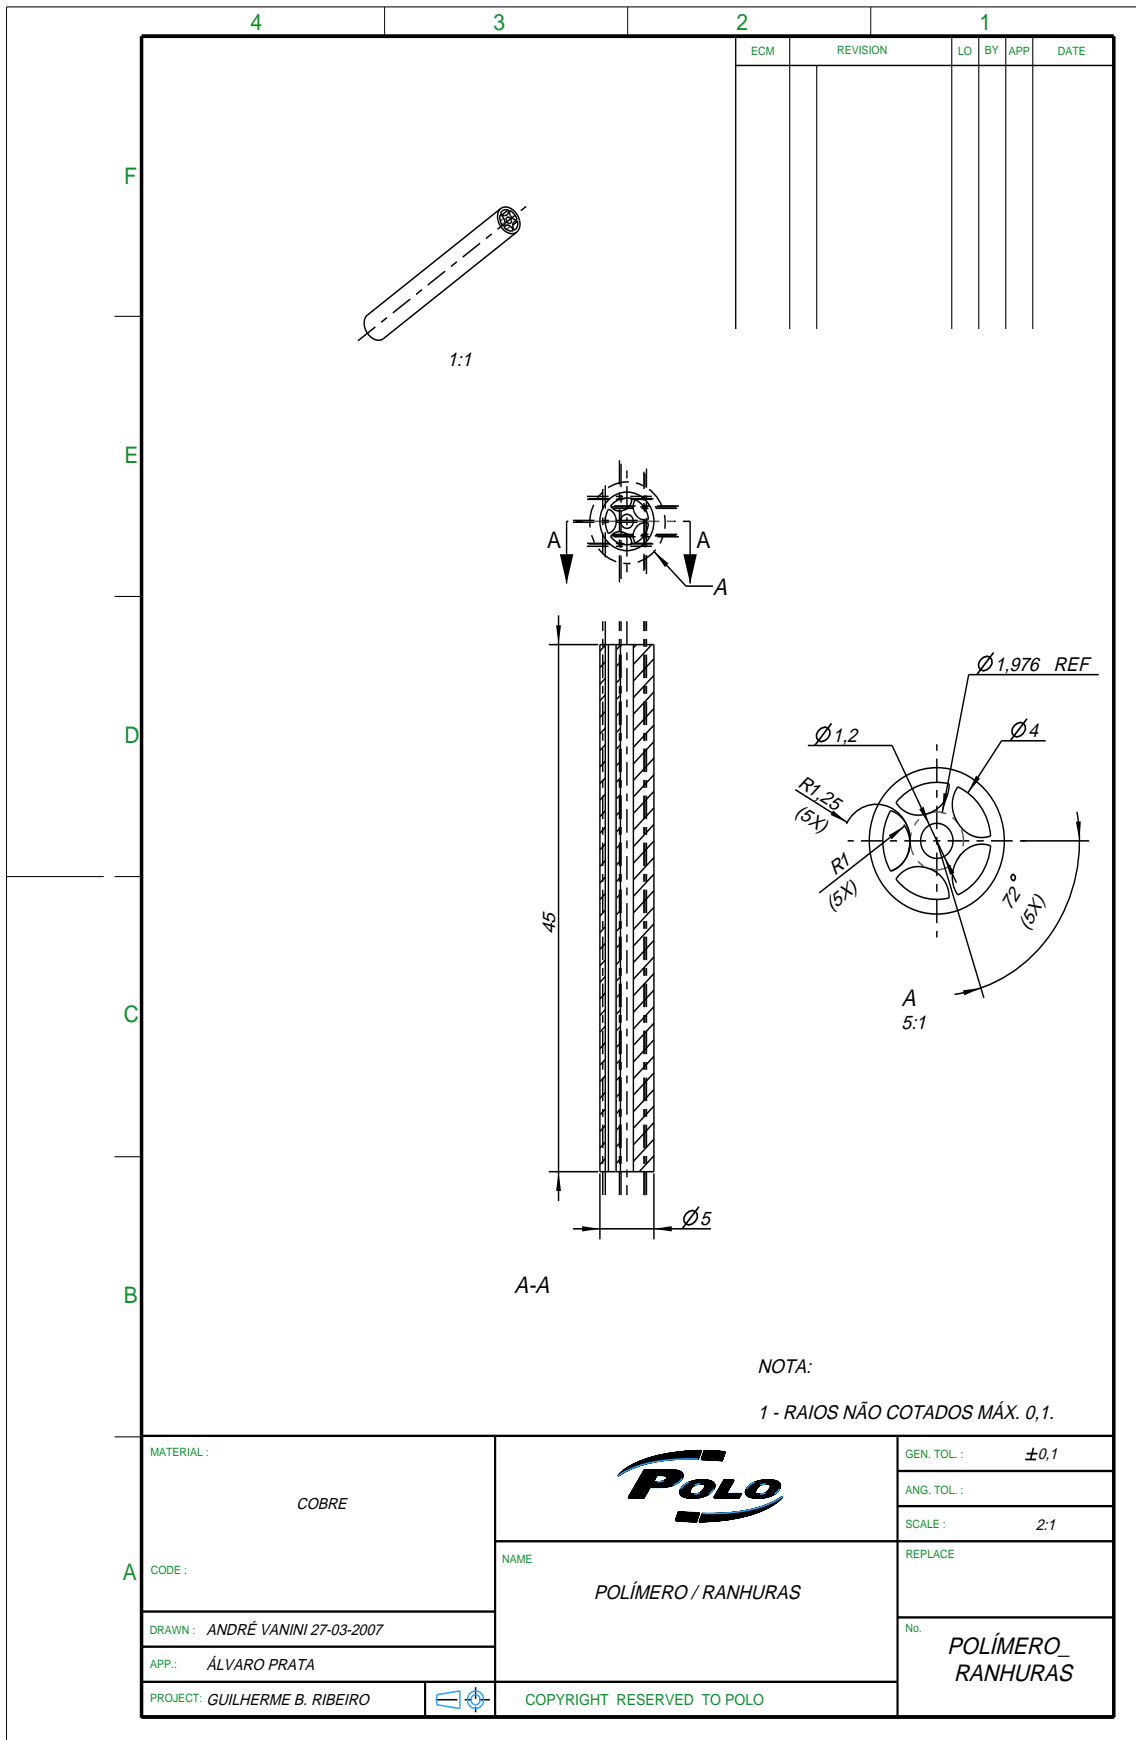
Desenho técnico do evaporador acoplado a tubos de calor - Parte III
